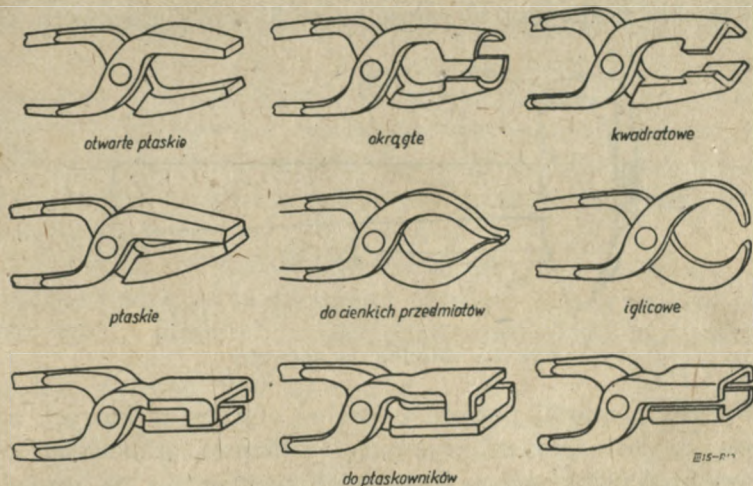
przedstawia kilka rodzajów szczęk kleszczy
